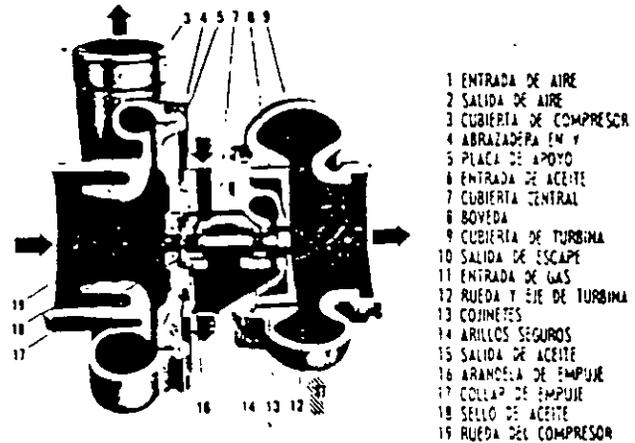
TA1 Corte seccional de turbocargador T-18-A
